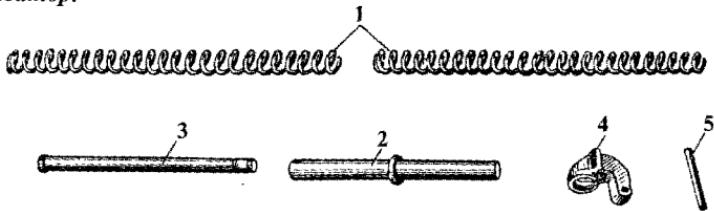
Возвратный механизм СВД-63: 1 - возвратные пружины; 2 — направляющая втулка; 3 — направляющий стержень; 4 — серьга; 5 — ось серьги.
